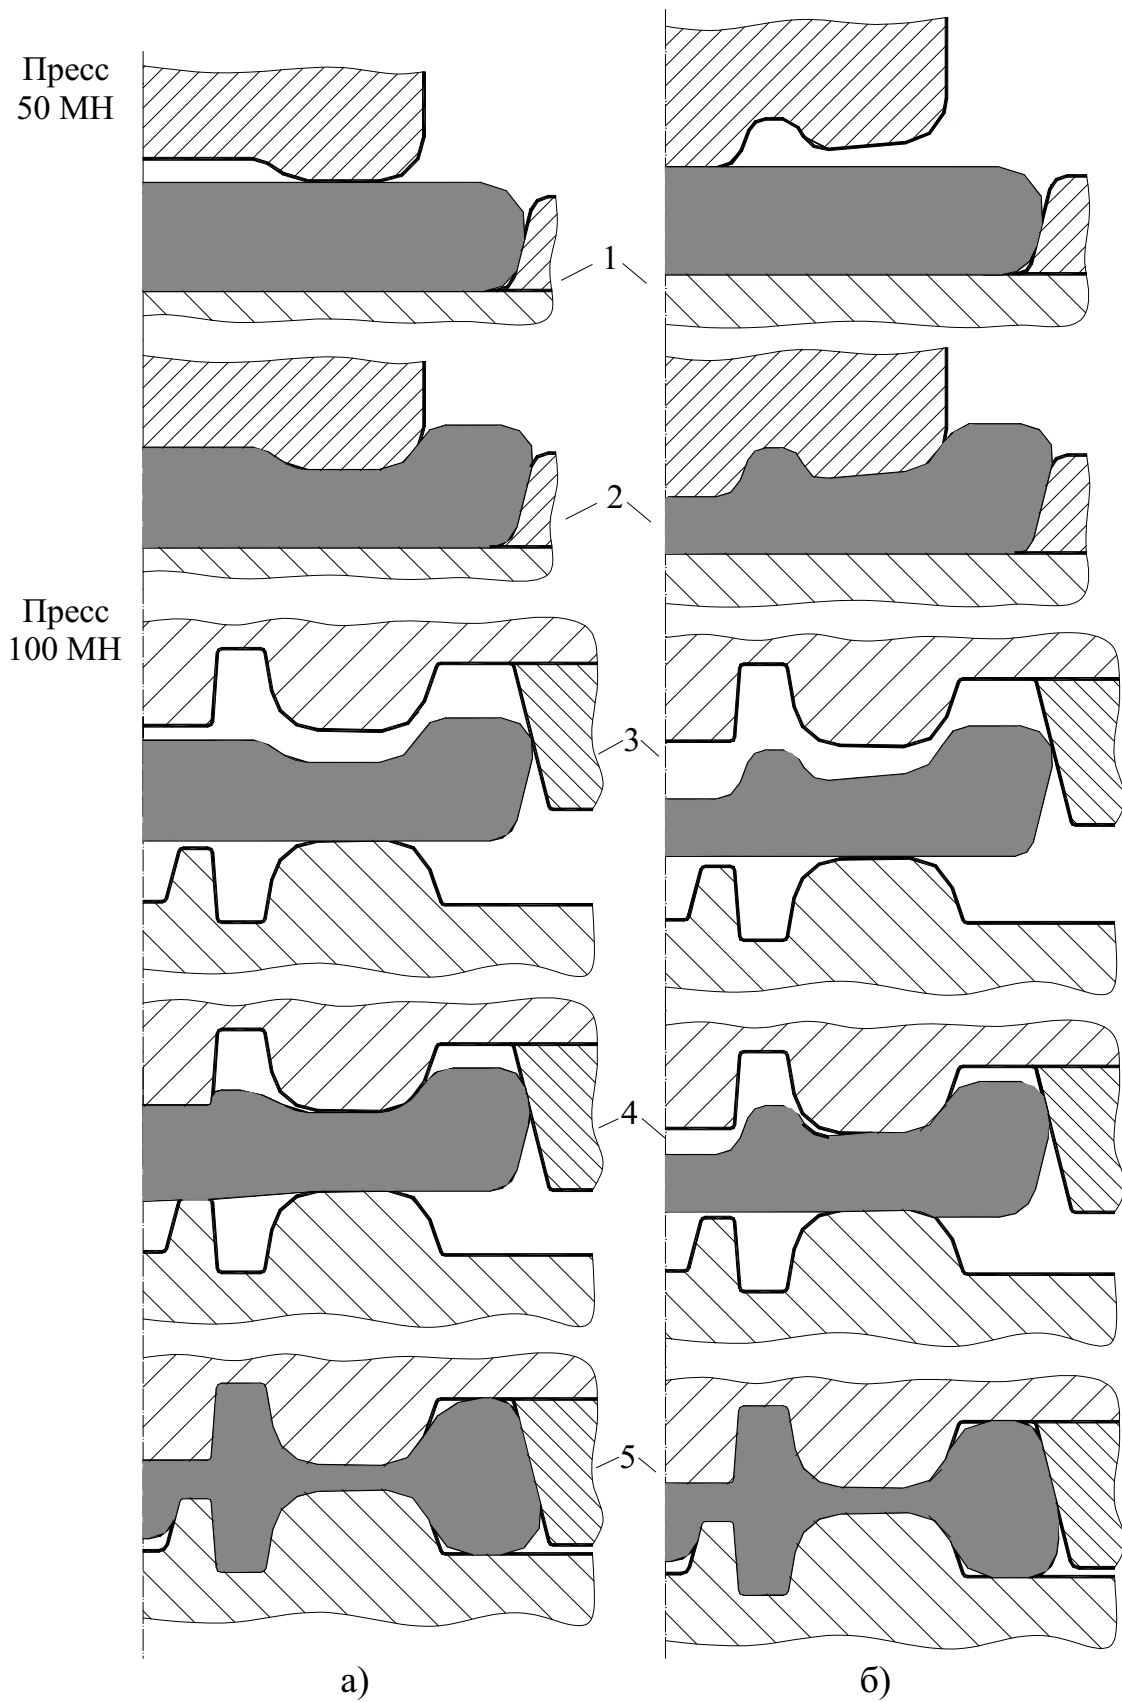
Схемы разгонки металла пуансоном с предварительным формированием части обода и ступицы и штамповки колесных заготовок.
